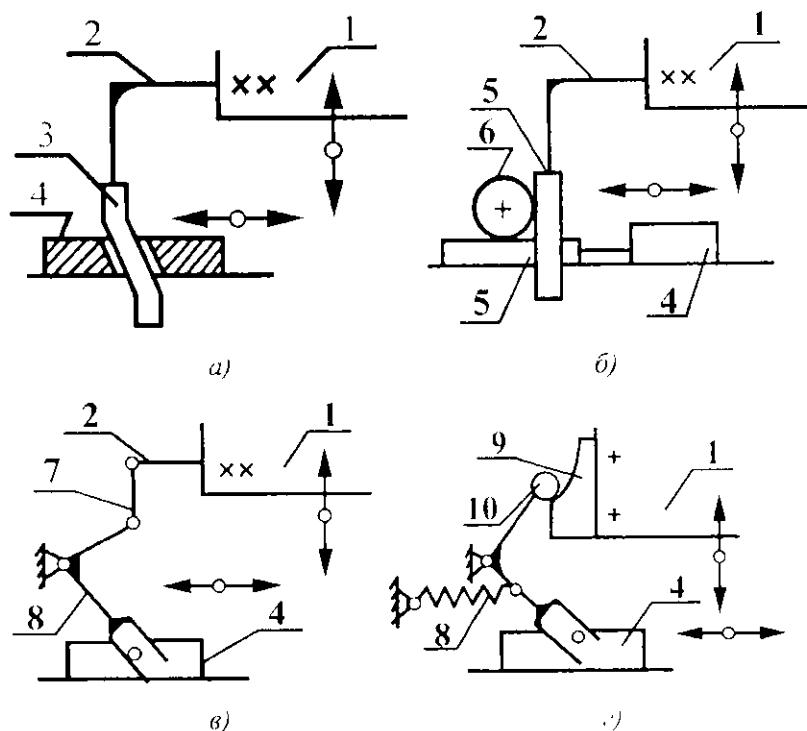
Схемы привода ползушки питателя от ползуна машины с помощью клина (а), рейки (б), рычага (в), кулачка (г): 1 - ползун, 2 - кривошип, 3 - клин, 4 - ползушка, 5 - рейка, 6 - зубчатое колесо, 7 - тяга, 8 - рычаг, 9 - кулачок, 10 - ролик
